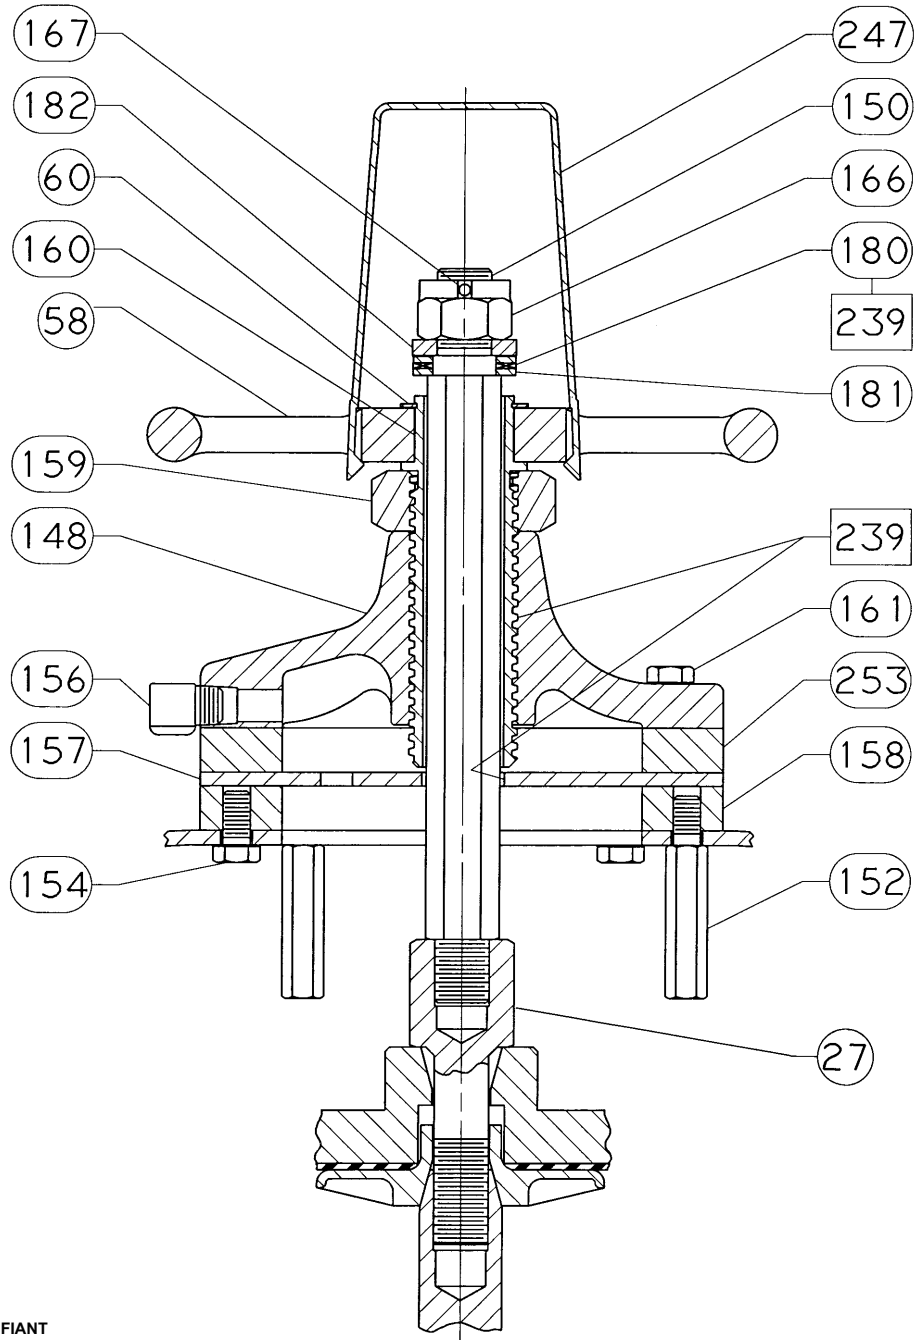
Ansamblu cu roată de mână montată deasupra, dispozitive de acțiune tipul P2 pentru dimensiuni de 45/45i, 50/50i, 60/60i, și 76/76i
